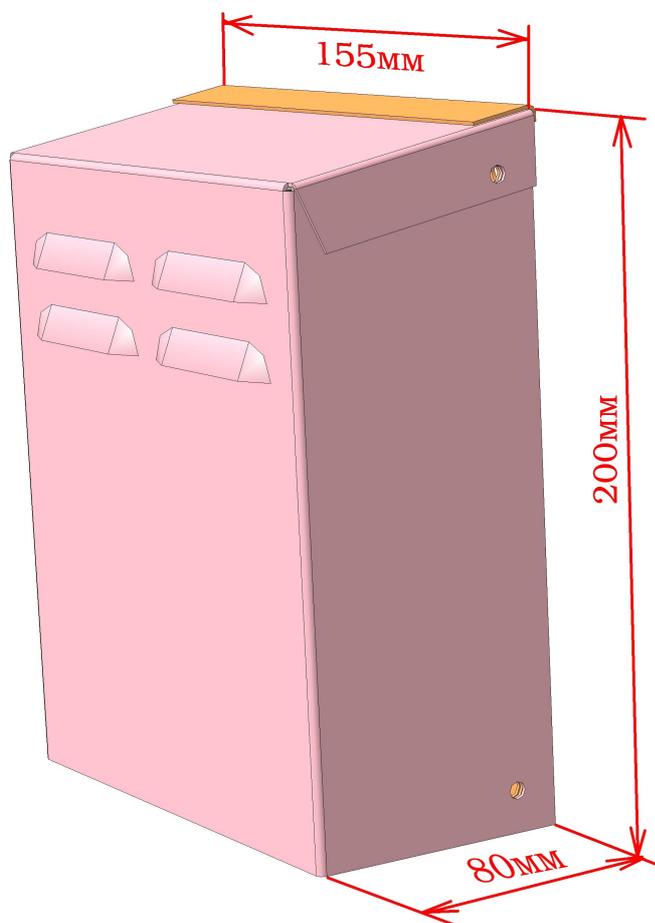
Внешний вид и габориты корпуса для АЛС-АУ
